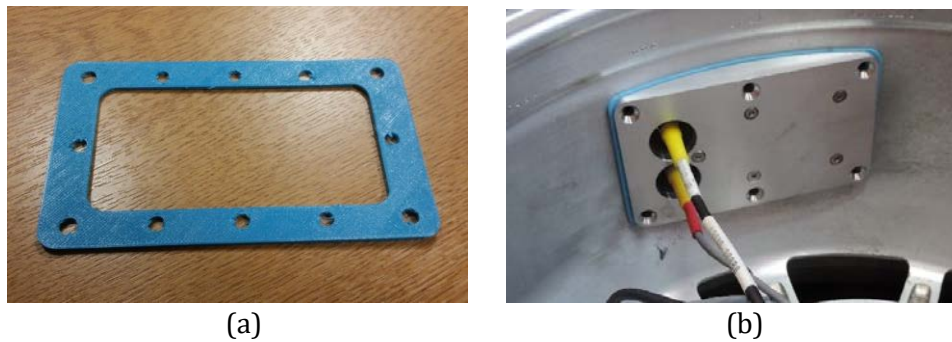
(a) Junta diseñada a medida, (b) junta instalada en el soporte.
